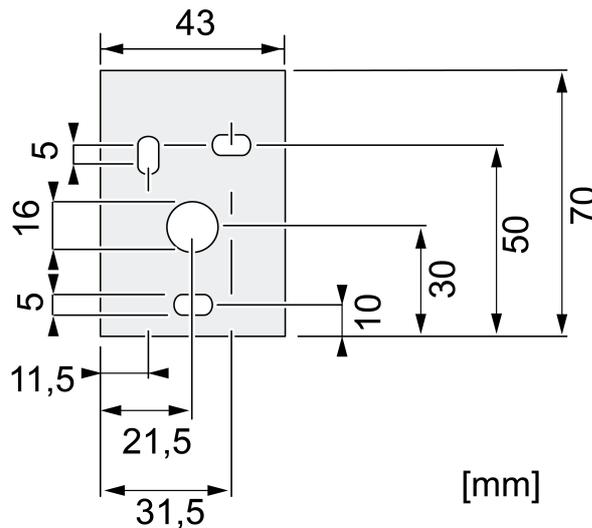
Braccio di fissaggio – Dimensioni dei fori
